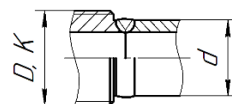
а – Стыковой сварной шов (код С)
